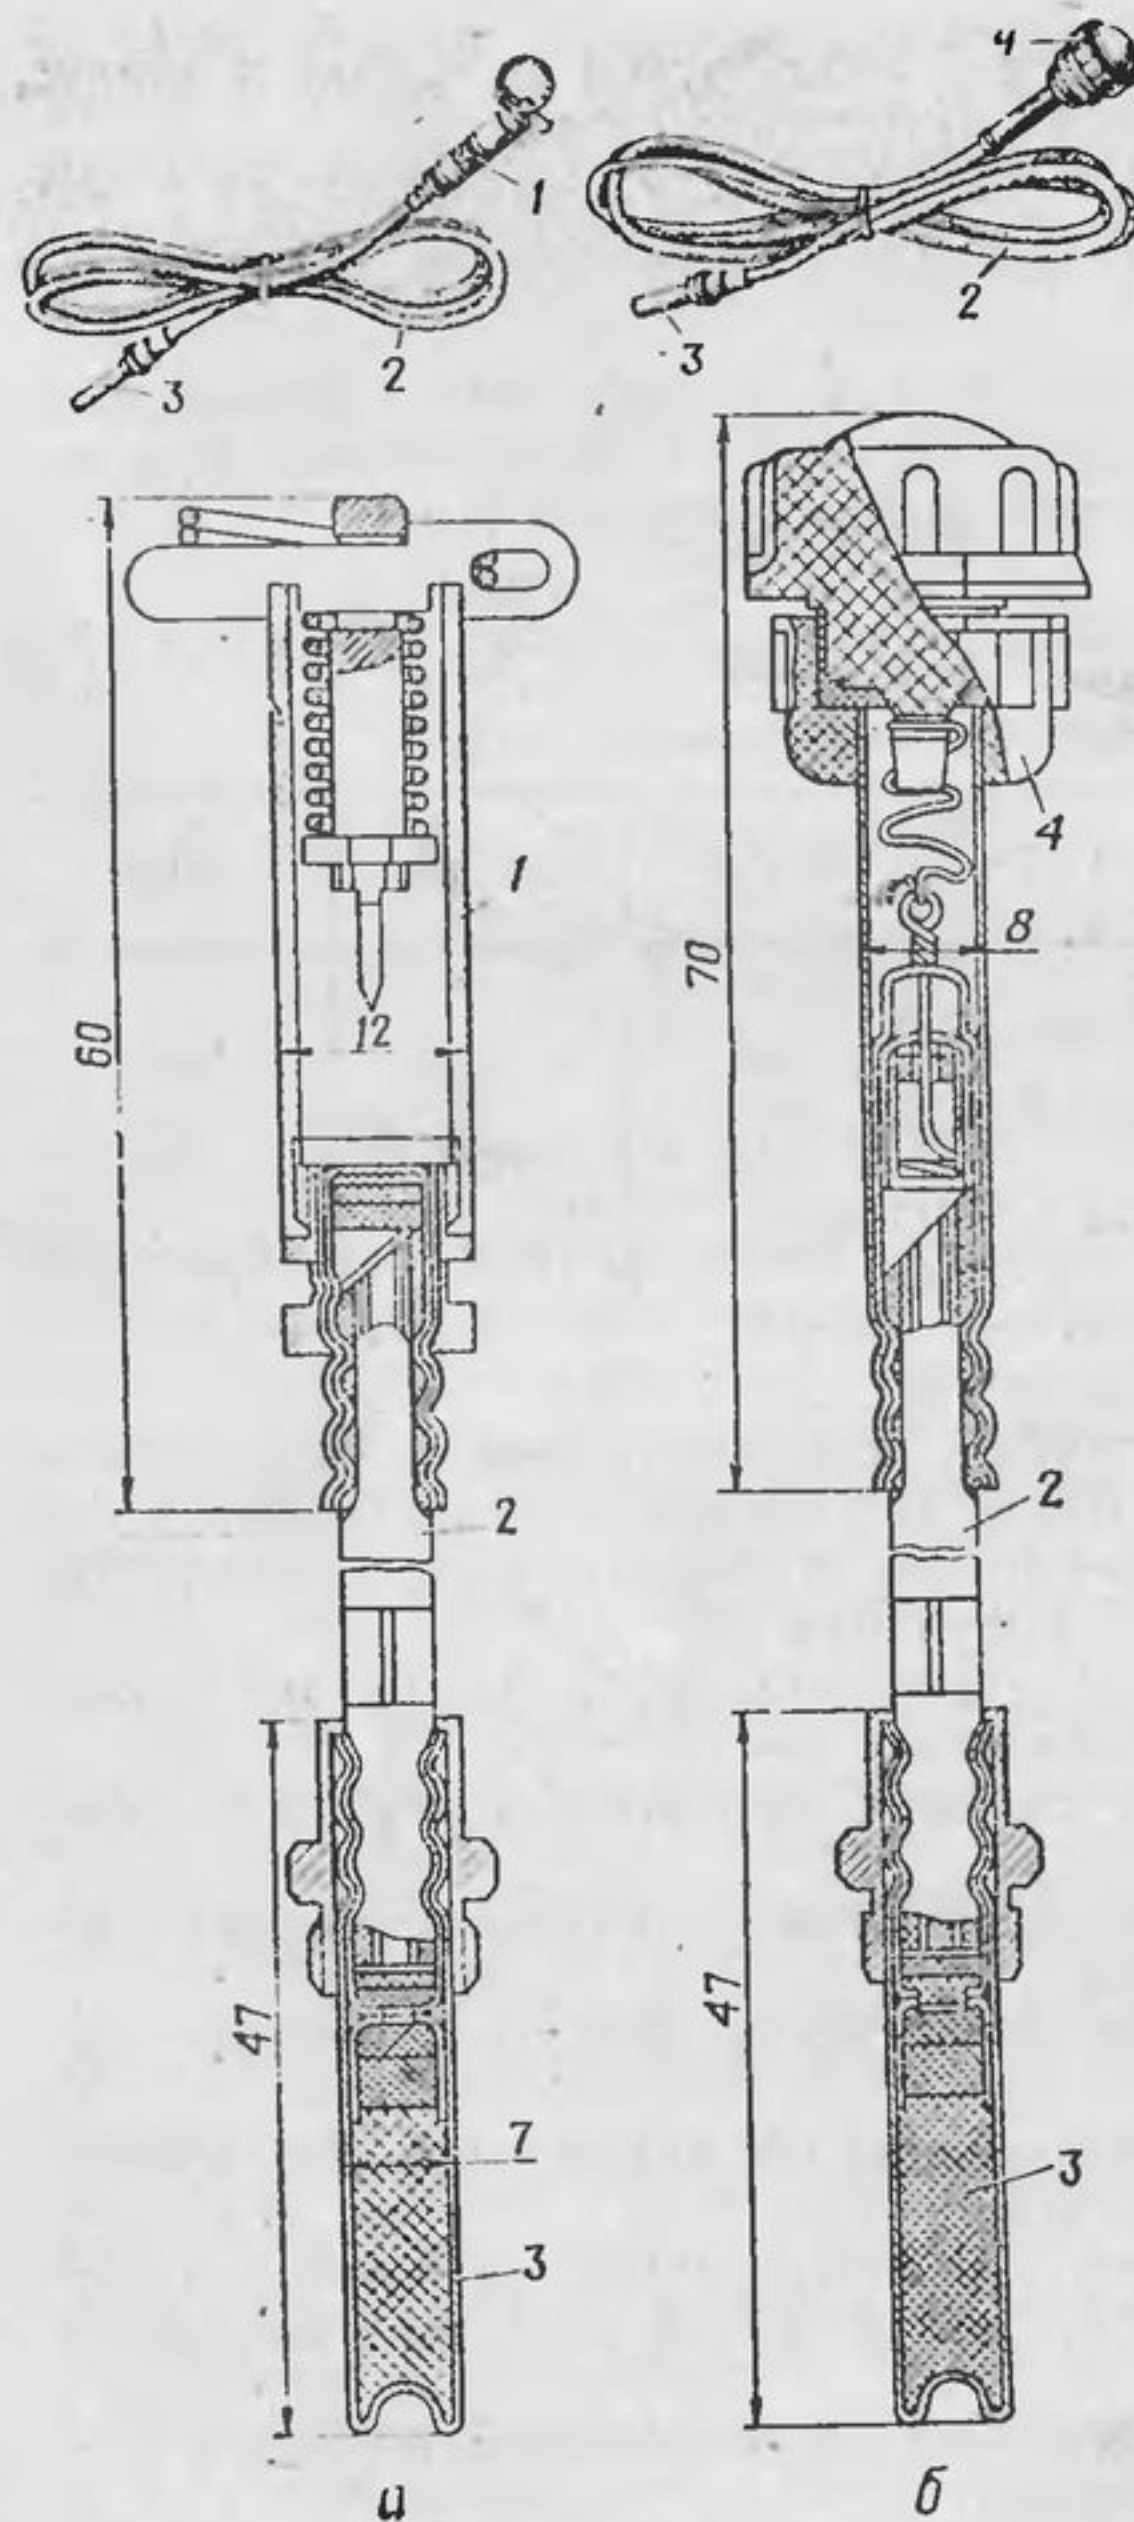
Зажигательные трубки промышленного изготовления (размеры в мм):
